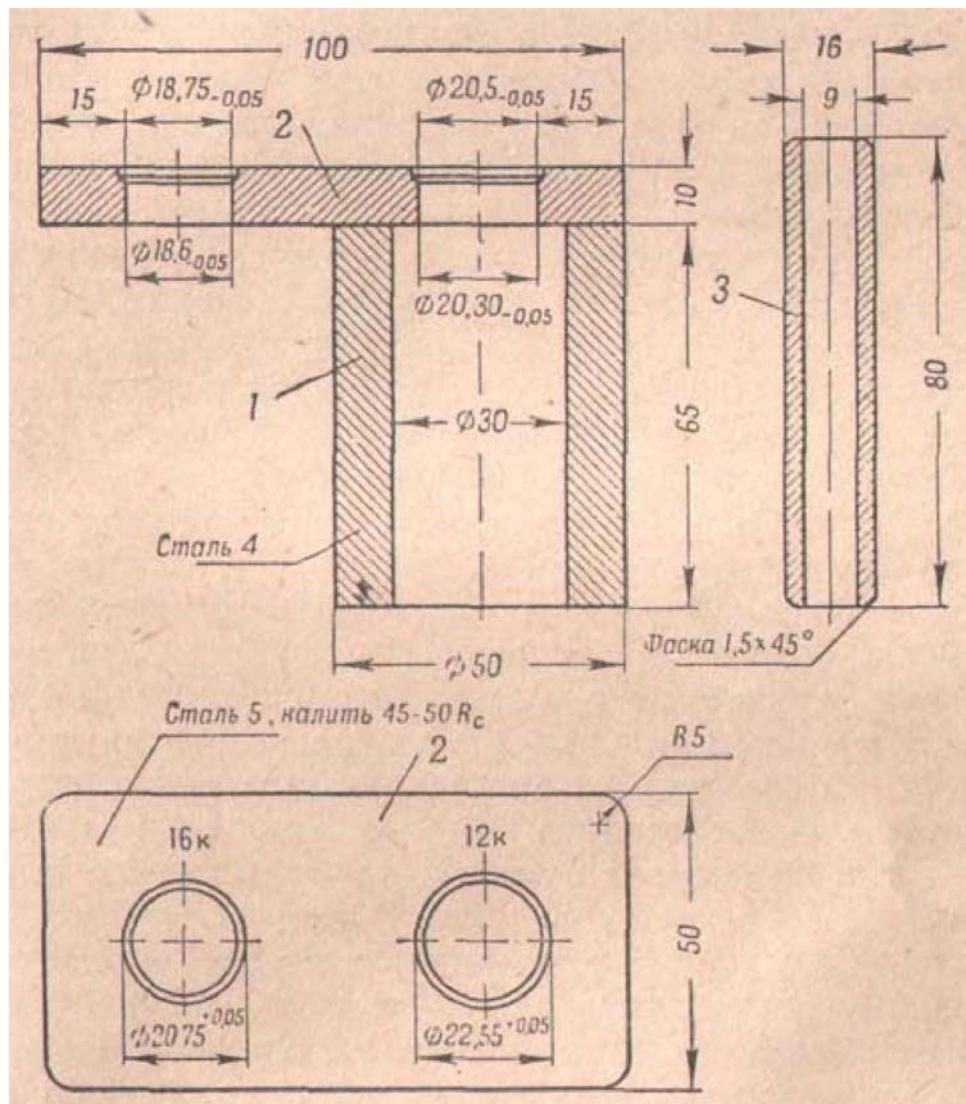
Набор инструментов для калибровки боковых стенок металлической головки бумажной гильзы: 1-подставка (металлическая); 2-стальная пластиинка с калибрующими отверстиями; надпись "калитъ 45-50R" означает, что калибрующую пластиинку надо закалить до твердости 45-60 единиц прибора Рокквела по шкале "С" (эти данные необходимы мастеру при изготовлении калибрующей пластиинки); 3-металлическая полая выколотка
